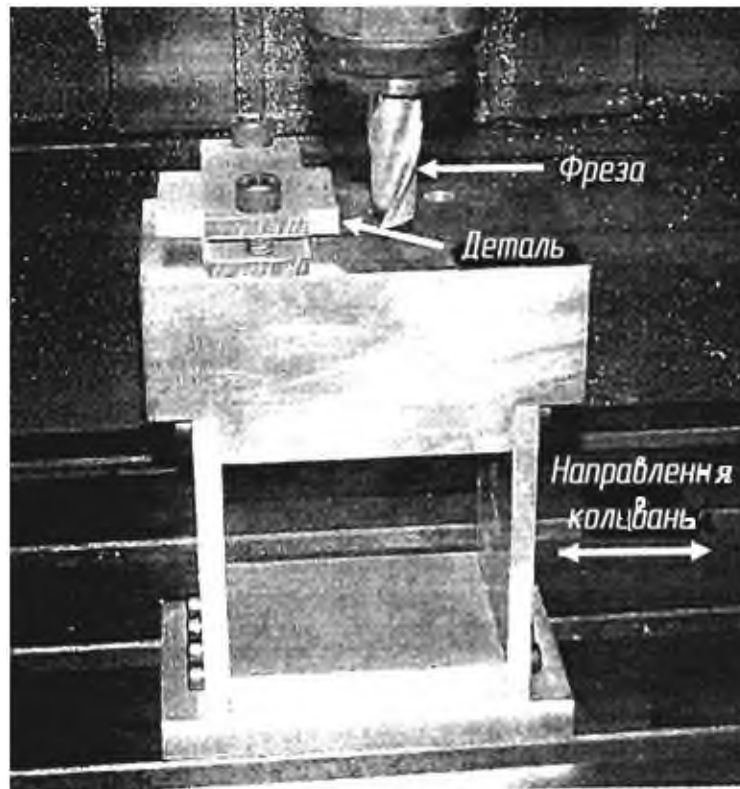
Пристрій для дослідження коливань при кінцевому фрезеруванні [36]
